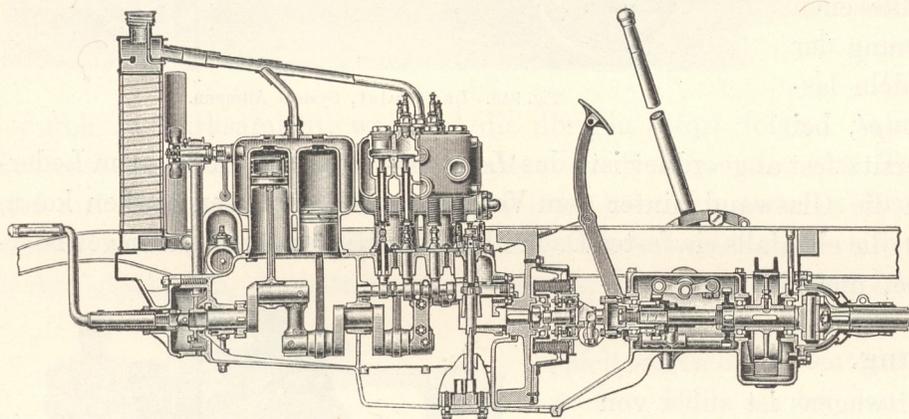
Schnitt durch den mit dem Getriebe zusammengebauten Motor eines Adler-Kleinautos.
